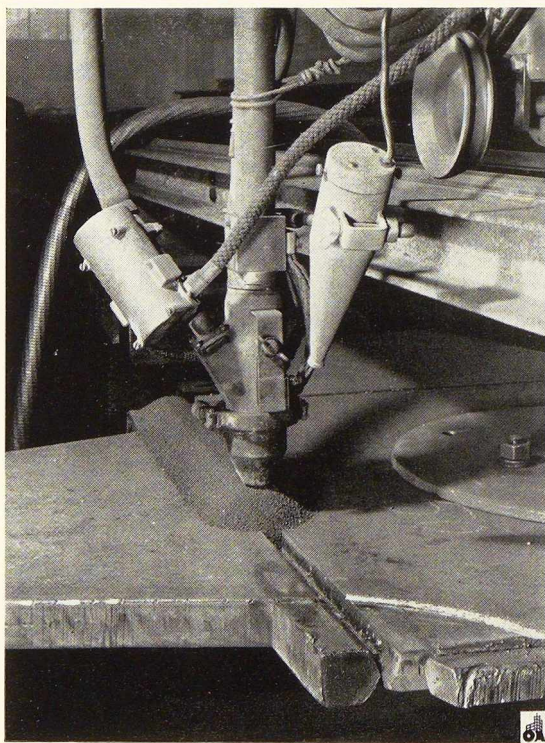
Soudure en atelier des tôles de gousset.
